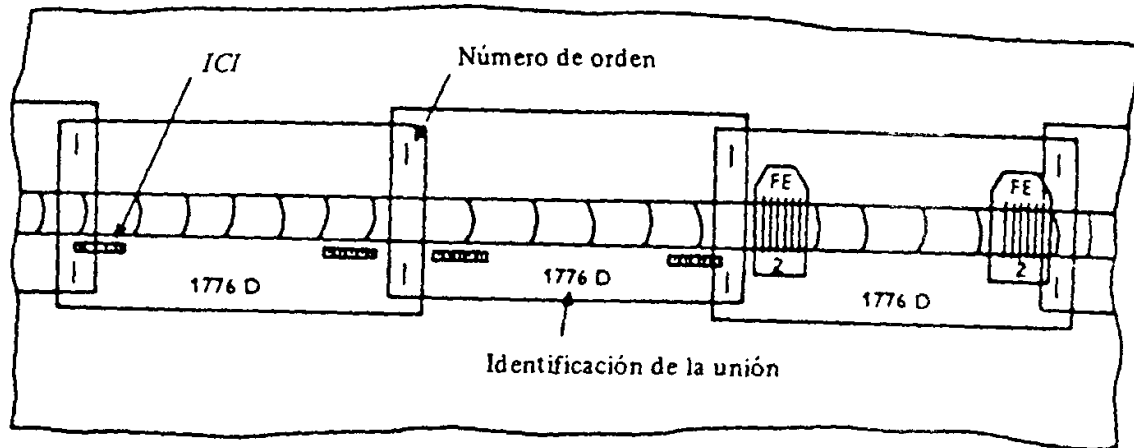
Radiografiado de soldaduras planas a tope.
